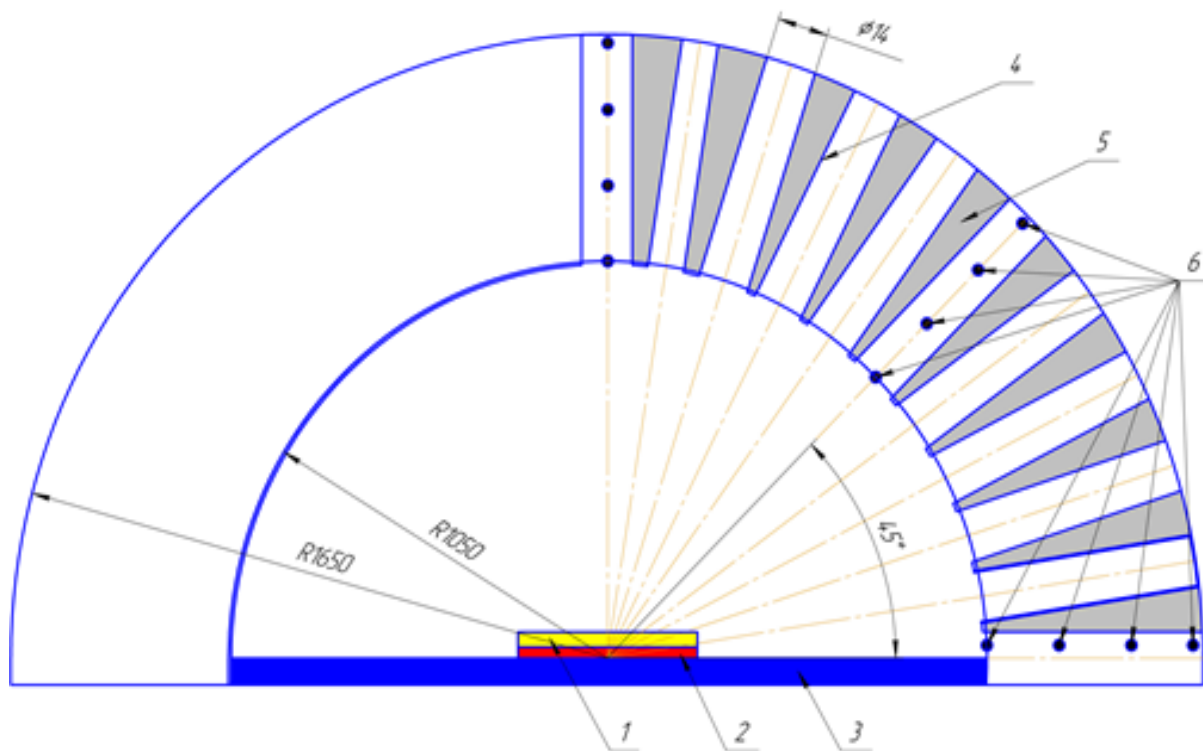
Схема поперечного перерізу трубчастої вибухової камери: 1 – заряд ВР, 2 – деталі, що зварюються, 3 – робочий стіл (плита), 4 – несучі елементи конструкції (труби), 5 – сипучий наповнювач, 6 – маркери
